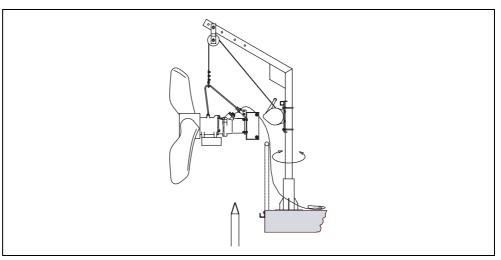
Maschine über das Führungsrrohrende schwenken
